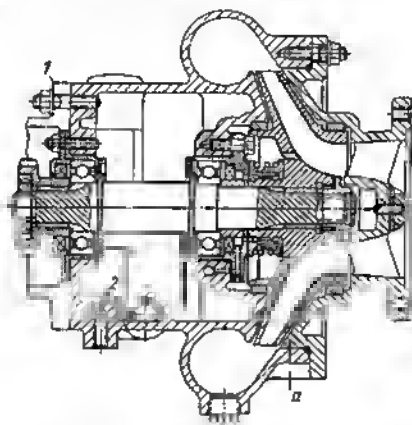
Vista general de una bomba con volutas de dimensiones disminuidas (dibujo de composición)
